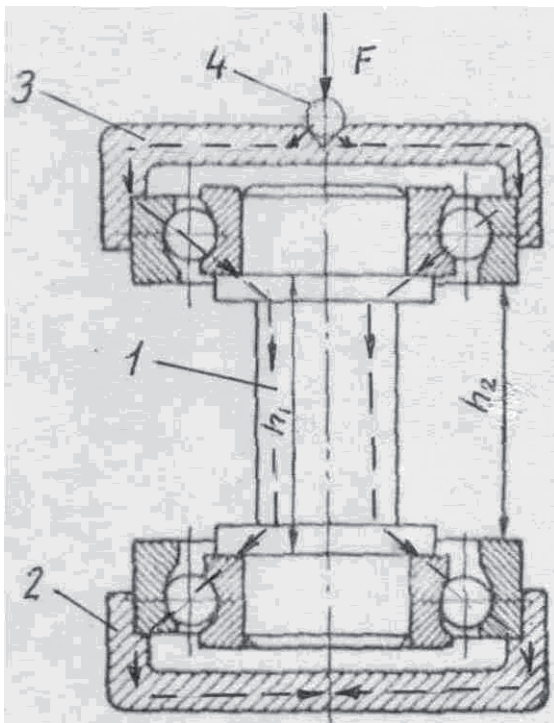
Создание предварительного натяга в двух подшипниках опоры вала
